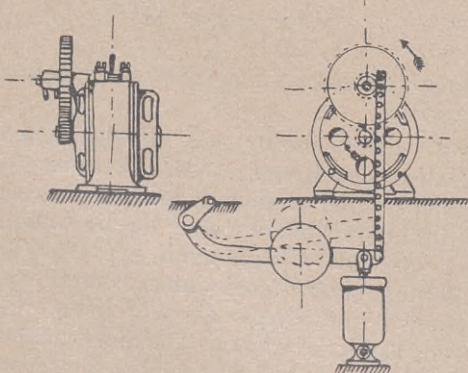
Motorbremsmagnet der E.-A. W. Lahmeyer & Co.
